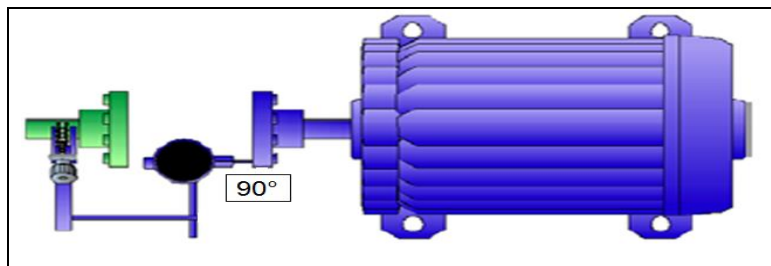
Posición 90° de medición FACE. Vista superior de motor.
